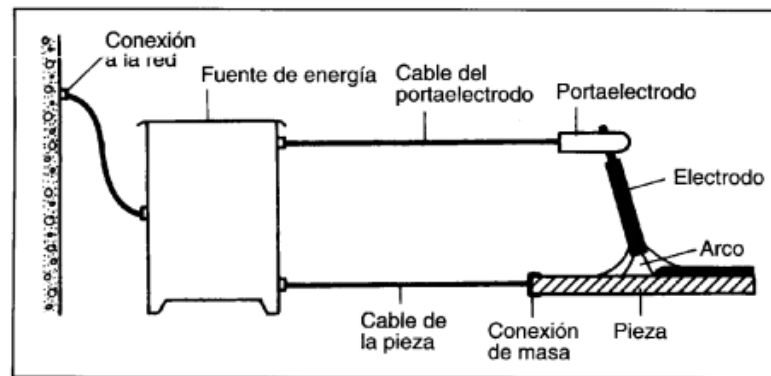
Equip de soldadura per arc amb elèctrode revestit. *Apunts Tecnologia Mecànica.
